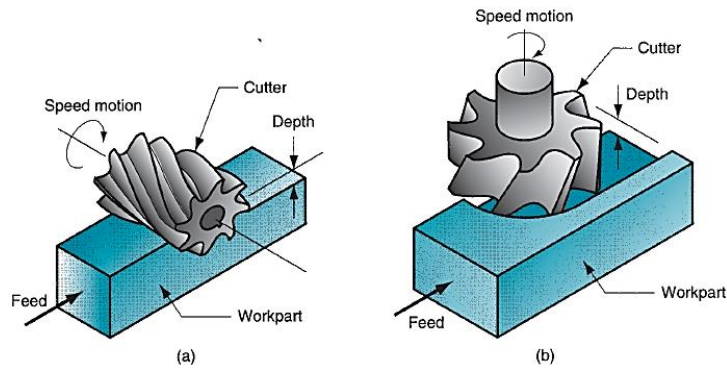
Diferentes processos de fresagem: a) tangencial ou cilíndrica ou periférica; b) de topo ou frontal [35]
